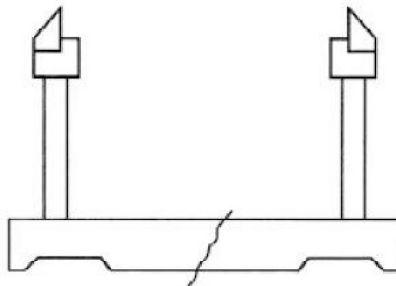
Приспособление для статической балансировки коленчатого вала с маховиком и сцеплением.
